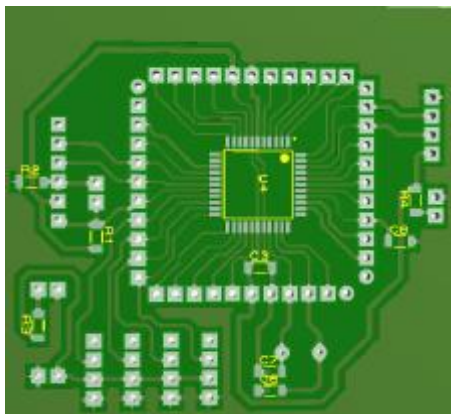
3D вид печатной платы микроконтроллерного блока робота-манипулятора
